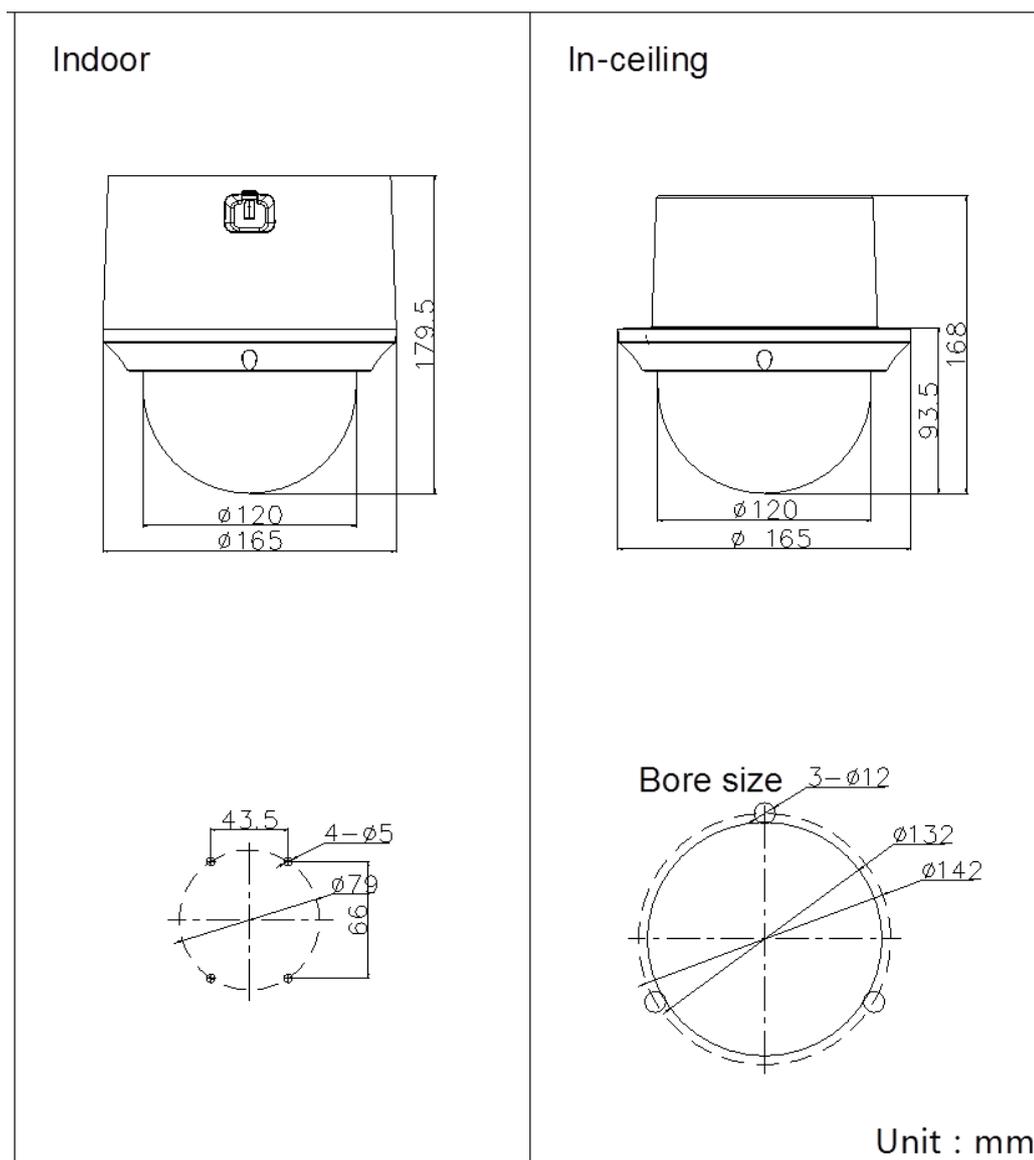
Габаритные размеры LTV-TSDNI23-M1
